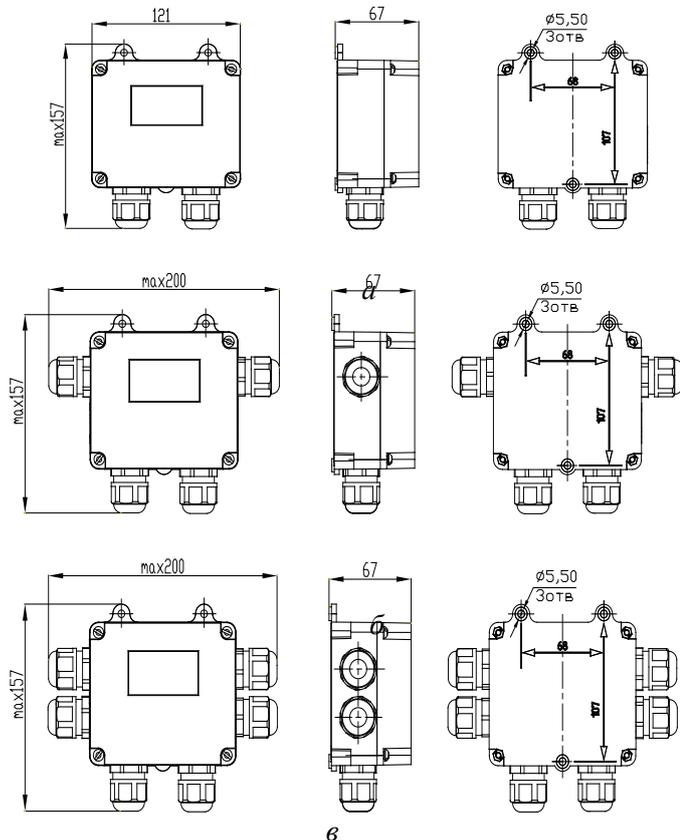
Установочные и габаритные размеры устройства соединительного.
